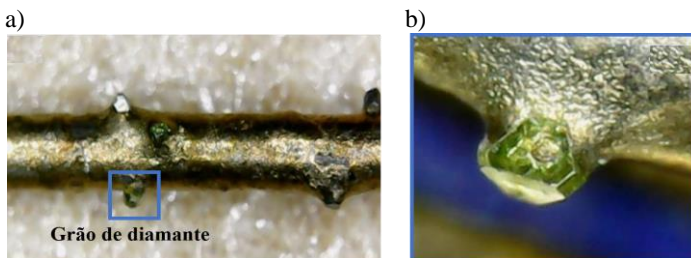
Fio diamantado brasado: a) superfície; b) grão de diamante sintético (adaptado de [50]).
